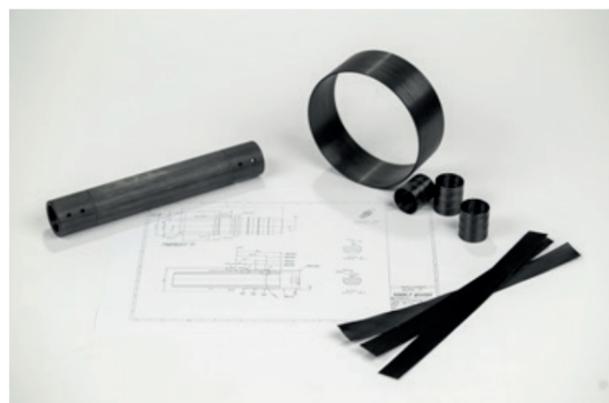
Zeichnung eines Connectorbauteils; gewickelte Halbzeuge; Tapematerial
